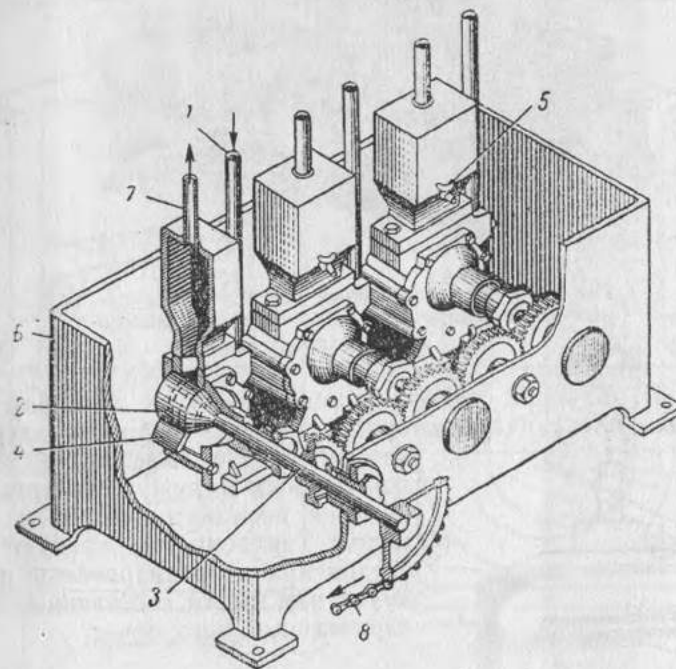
Тройной пластинчато-роторный насос ММЗ.
